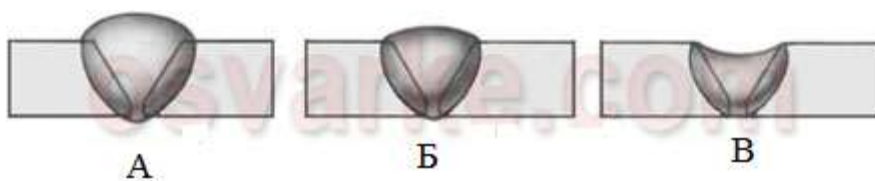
Сварные швы по форме наружной поверхности.
